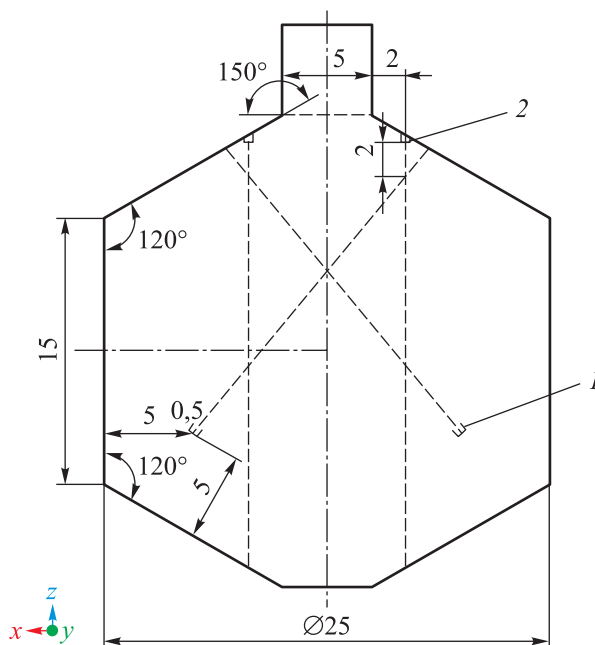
Схема конструкции камеры охлаждения порошка, имеющей плавные своды
